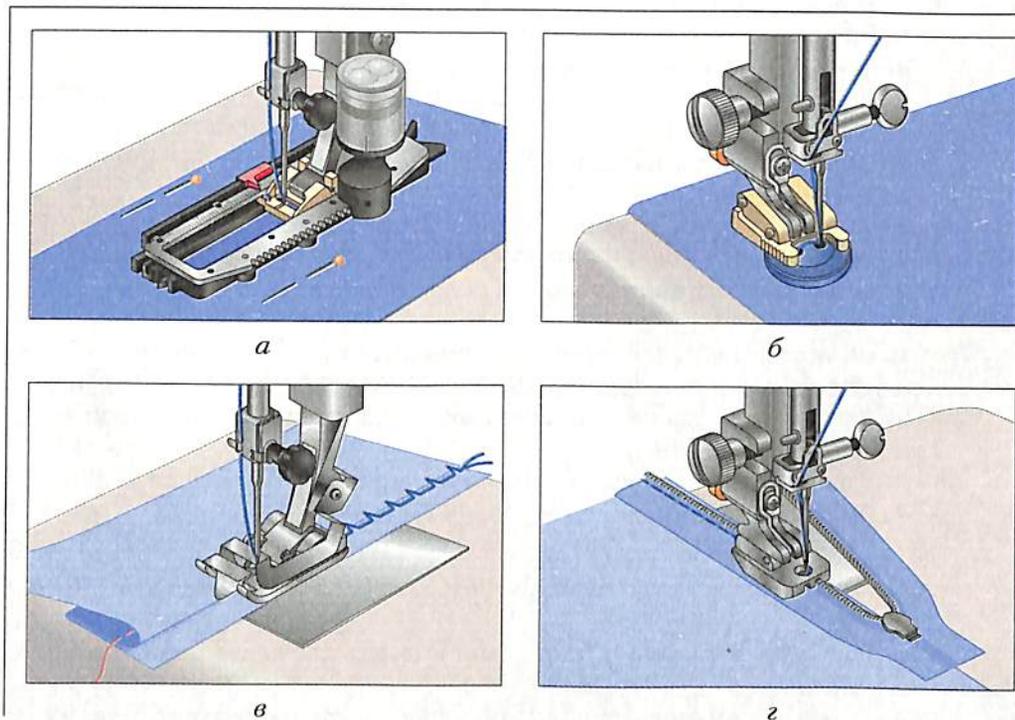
Приспособления к швейной машине: а – лапка для обмётывания петель; б – лапка для пришивания пуговиц; в – лапка для потайного подшивания; z – лапка для притачивания потайной застёжки-молнии
